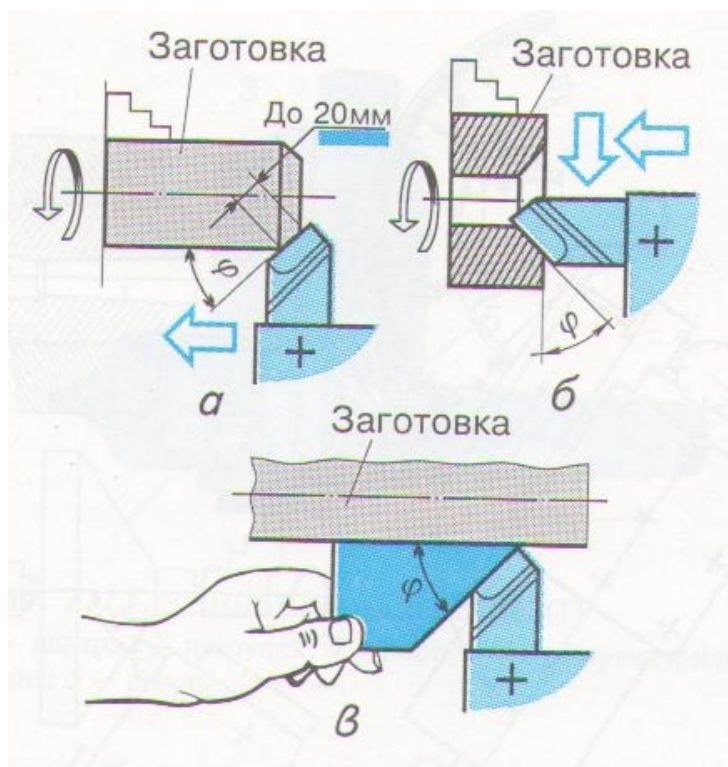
Обробка коротких конічних поверхонь широким різцем:
